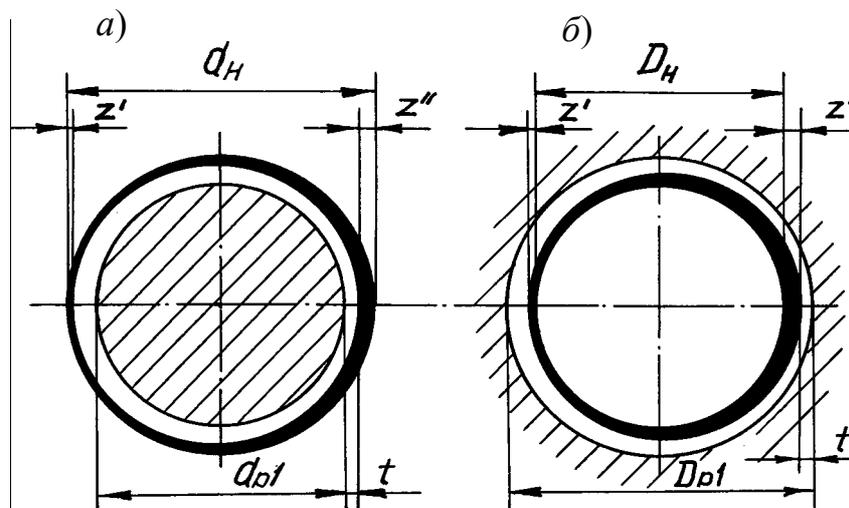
Схема определения ремонтных размеров: а – для вала; б – для отверстия
